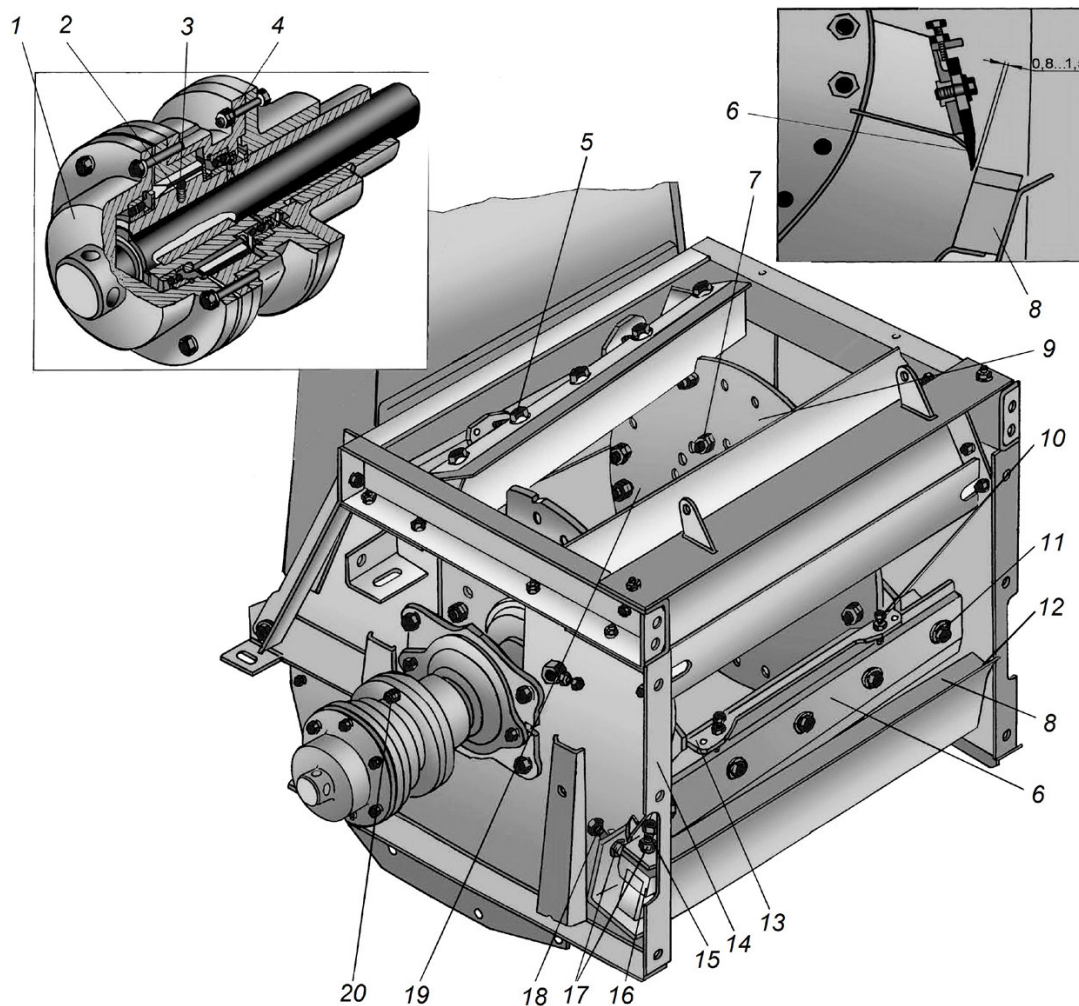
Измельчающий аппарат: 1 – крышка обгонной муфты; 2 – пружина; 3 – шарик; 4 – корпус; 5 – болт крепления ножа; 6 – нож; 7 – болт крепления опоры ножа; 8 – противорежущий брус; 9 – диск; 10 – установочный винт; 11 – прижим ножа; 12 – чистик; 13 – опора ножа; 14 – рама; 15 – прижимной болт; 16 – прижим; 17 – контргайка; 18 – регулировочный болт; 19 – барабан; 20 – предохранительный болт
